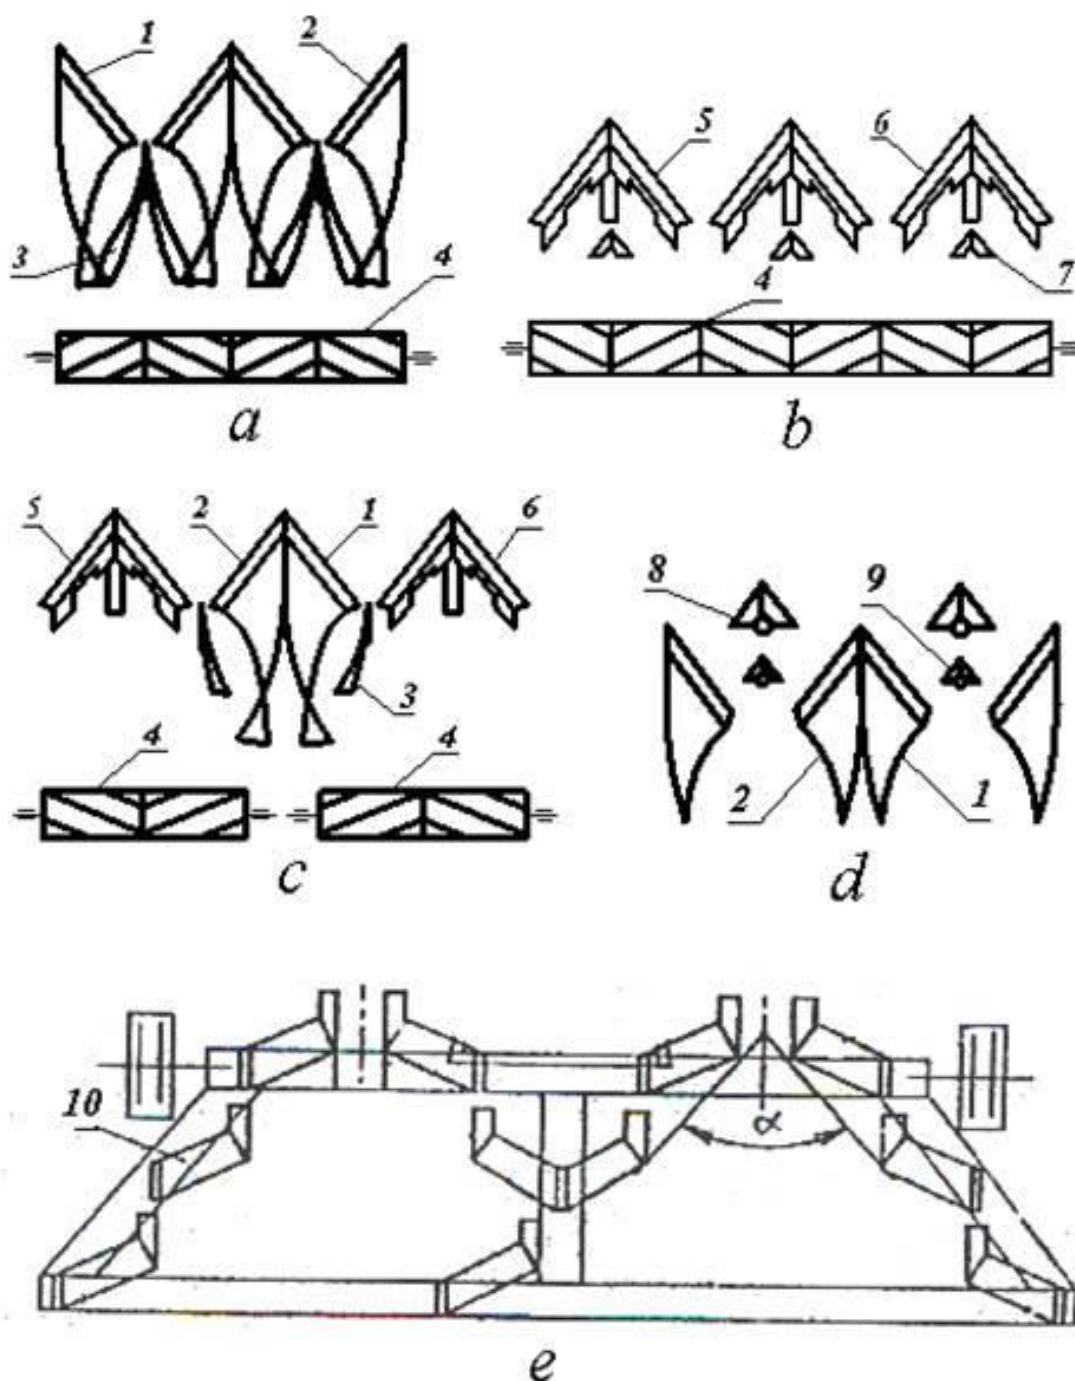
Схема multifункционального почвообрабатывающего агрегата.
